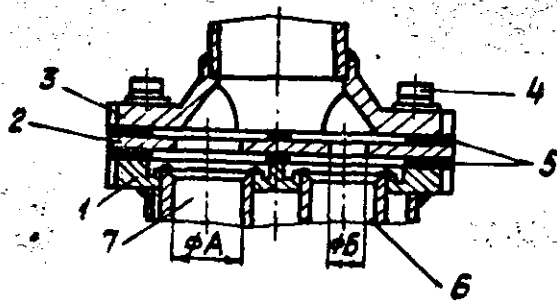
Регулировочный узел суфлирования лабиринтов корпуса камеры сгорания:
